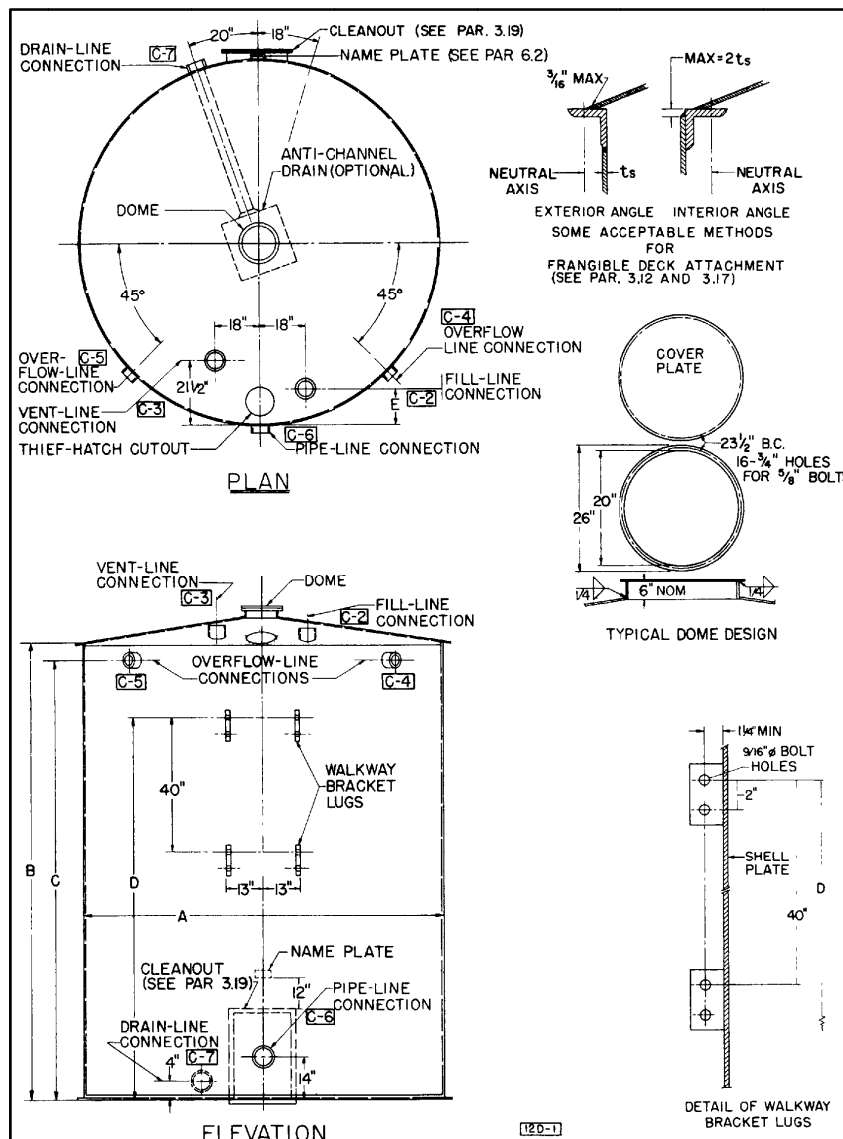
Dimensionamiento y configuración de tanques de almacenamiento según API 12D [28]
